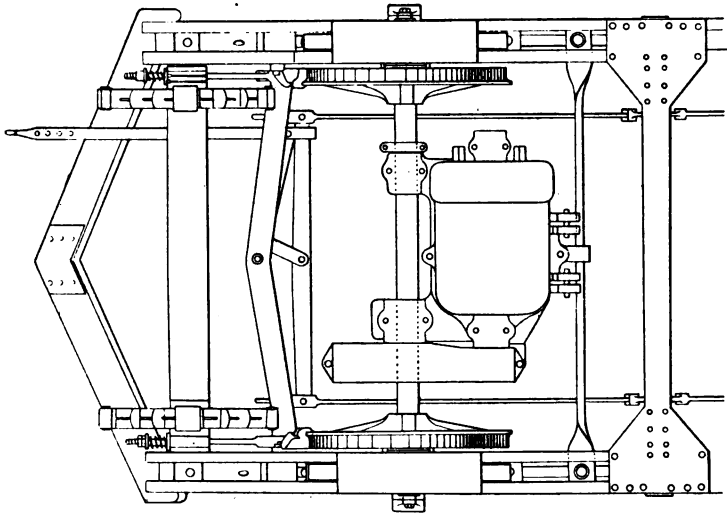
Montage du moteur sur le truck. — Vue en plan.
